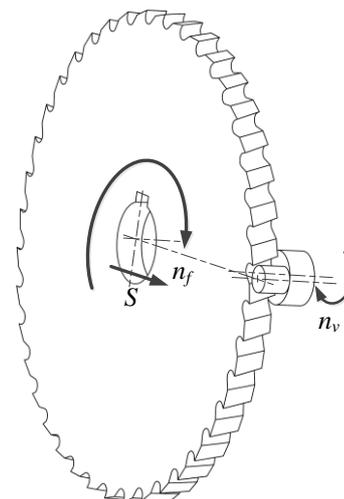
Обработка эксцентриковых шеек фрезой-протяжкой
